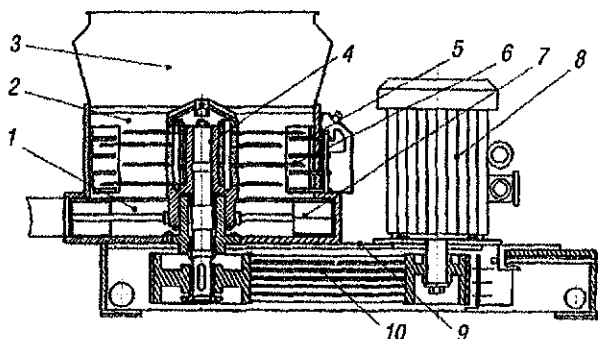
Схема измельчителя-смесителя кормов ИСК-3: 1 – выгрузная камера; 2 – рабочая камера; 3 – приемная камера; 4 – ротор; 5 – пакет противорезов; 6 – нож; 7 – швырялка; 8 – электродвигатель; 9 – рама; 10 – клиноременная передача
